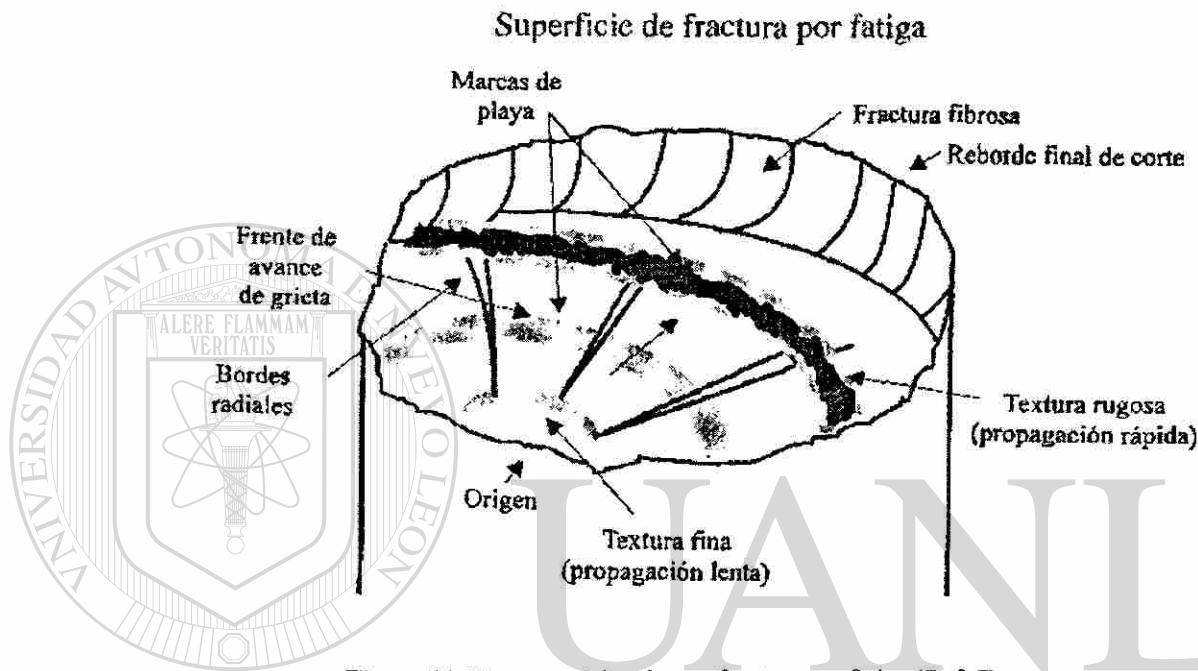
Esquema típico de una fractura por fatiga (Ref. 7).
